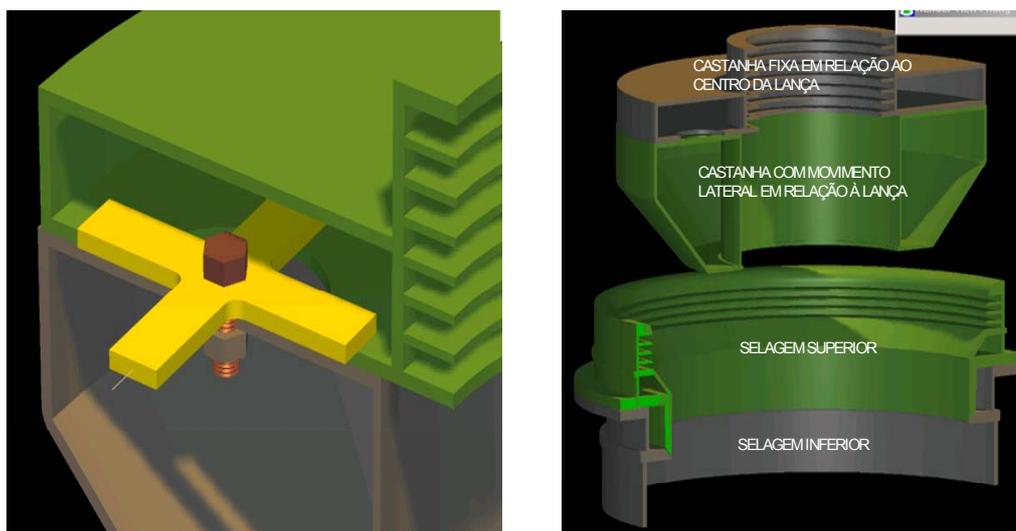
Castanha fixa e castanha deslizante – cruzeta
